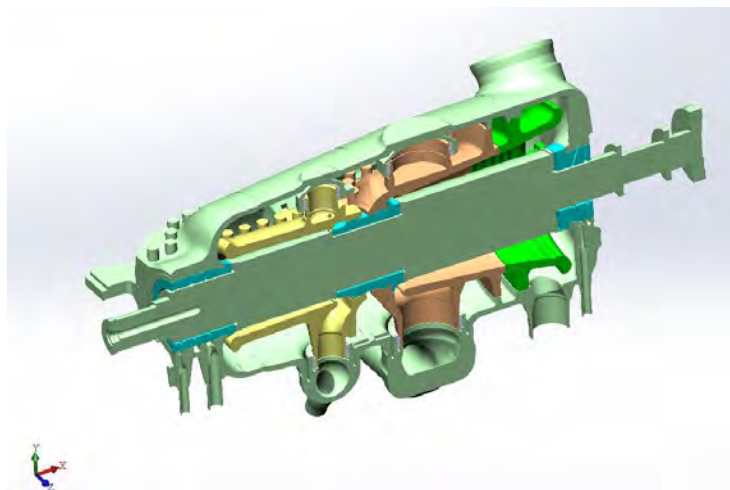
Геометрическая модель корпуса ЦВСД К-130-12,8 с внутренними элементами
